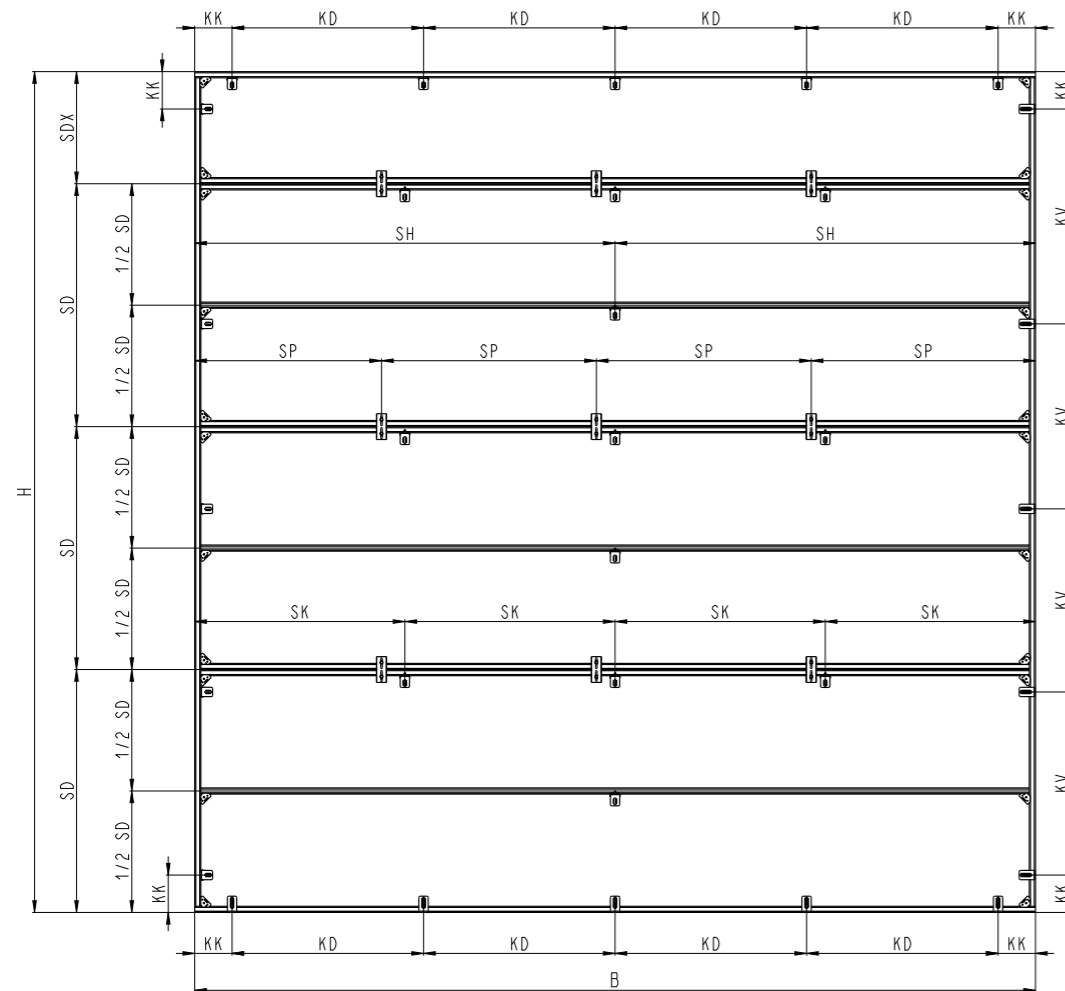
Princip skládání základních bloků stěn do výsledných konstrukcí širších než 4,5 m
